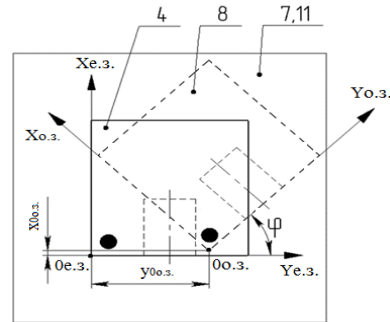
Зображення оброблюваної заготовки, на яке накладено зображення еталонної заготовки
